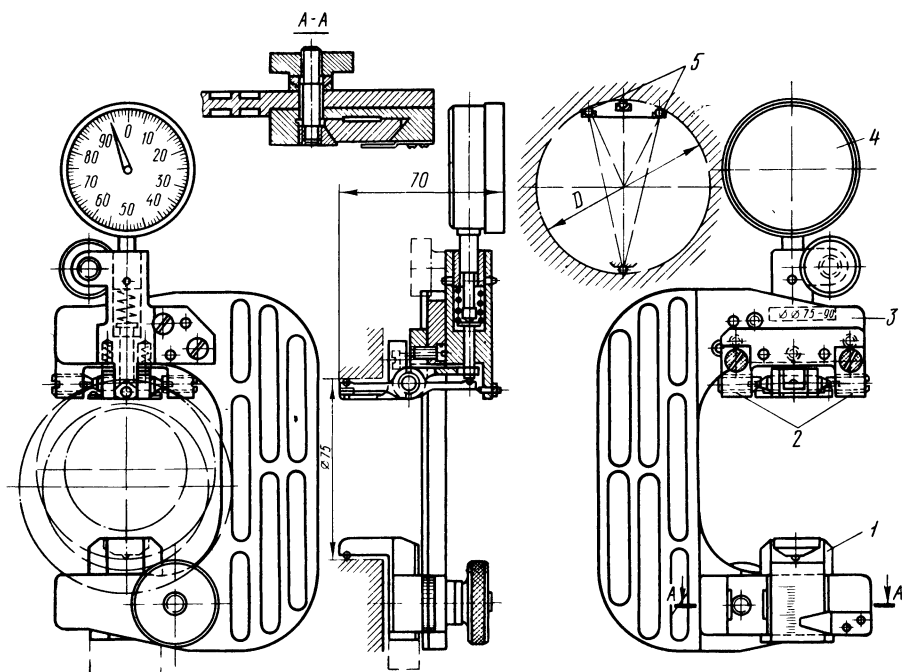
Индикаторная скоба для проверки отверстий без съема борштанги
